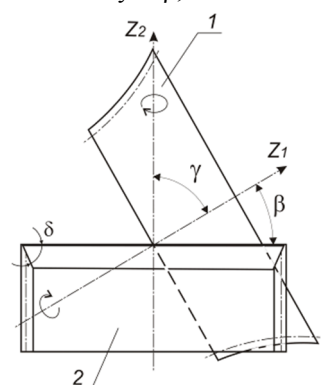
Схема изготовления квазиглобoidного колеса
